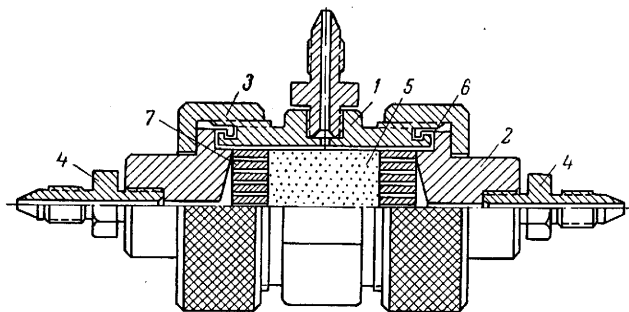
Общий вид кернодержателя с всесторонним обжимом образца породы.
